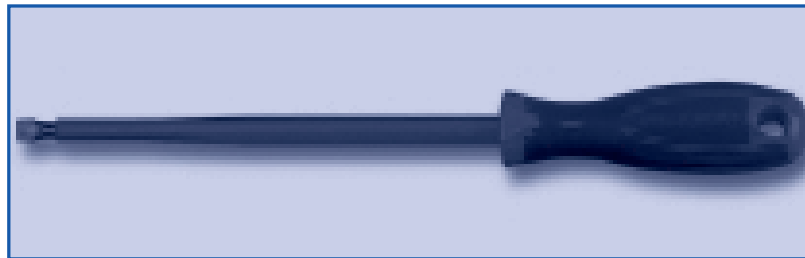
destornillador punta plana o ranura con aislamiento.
